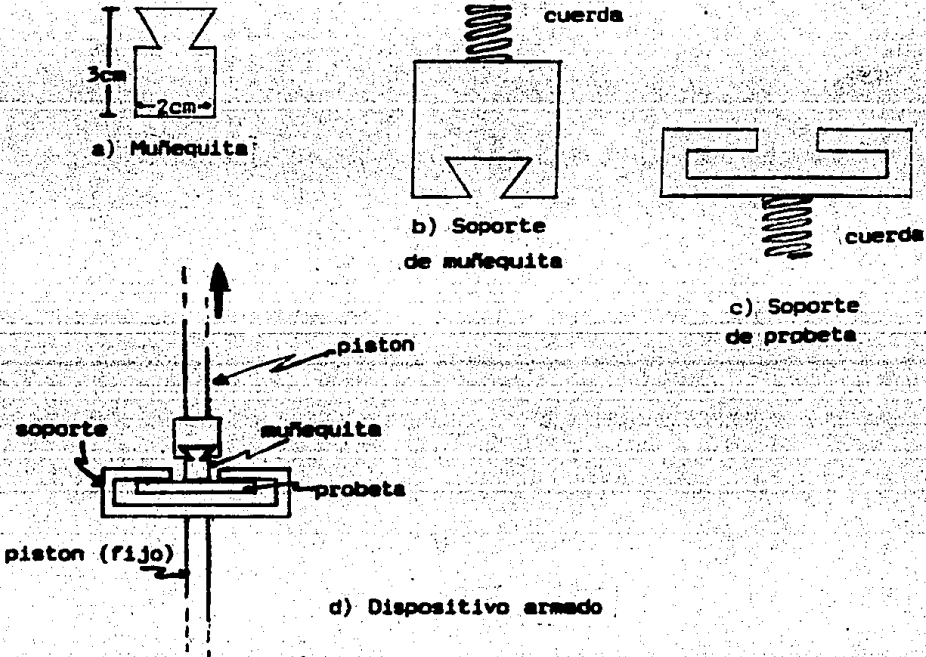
Dispositivo (d) utilizado para las pruebas de adhesión. El pistón tensa, hasta que se separe la muñeca de la probeta.
